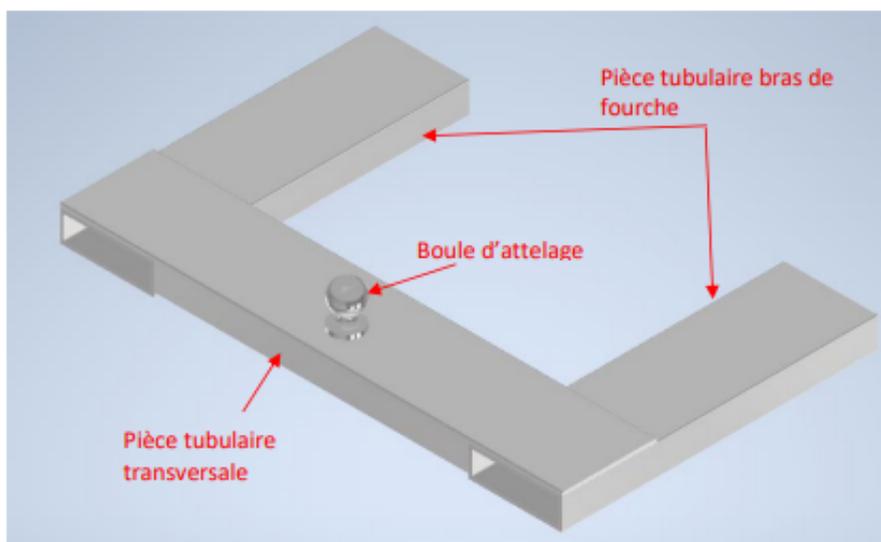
Composants du sous-ensemble de l'accessoire de remorquage
